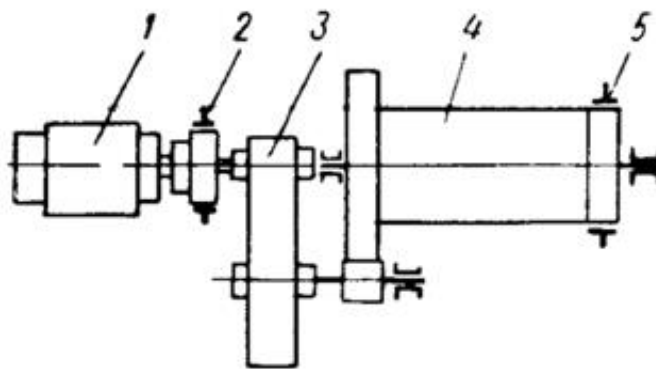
Кинематическая схема однодвигательной скиповой лебёдки
